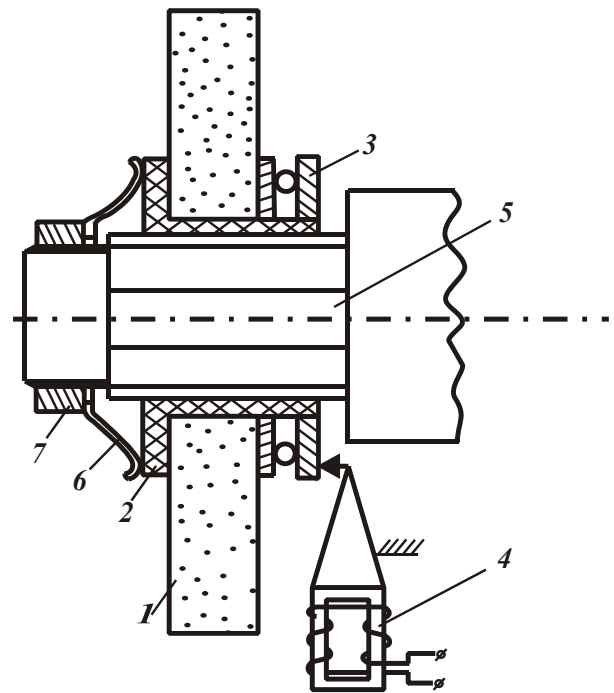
Устройство с осевым перемещением шлифовального круга (колебательная система крепится за фланец концентратора): 1 – круг; 2 – шлицевая втулка; 3 – подшипник; 4 – магнитострикционная колебательная система; 5 – шлицевый вал; 6 – пружина; 7 – гайка.
